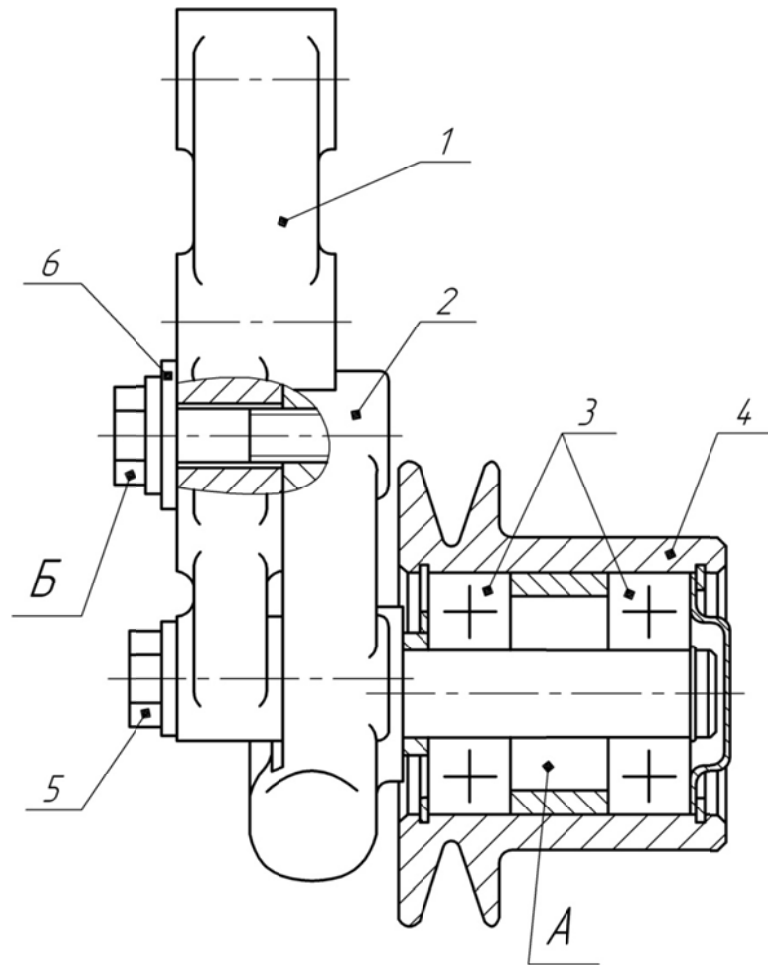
Натяжное устройство 236-1307155-А
